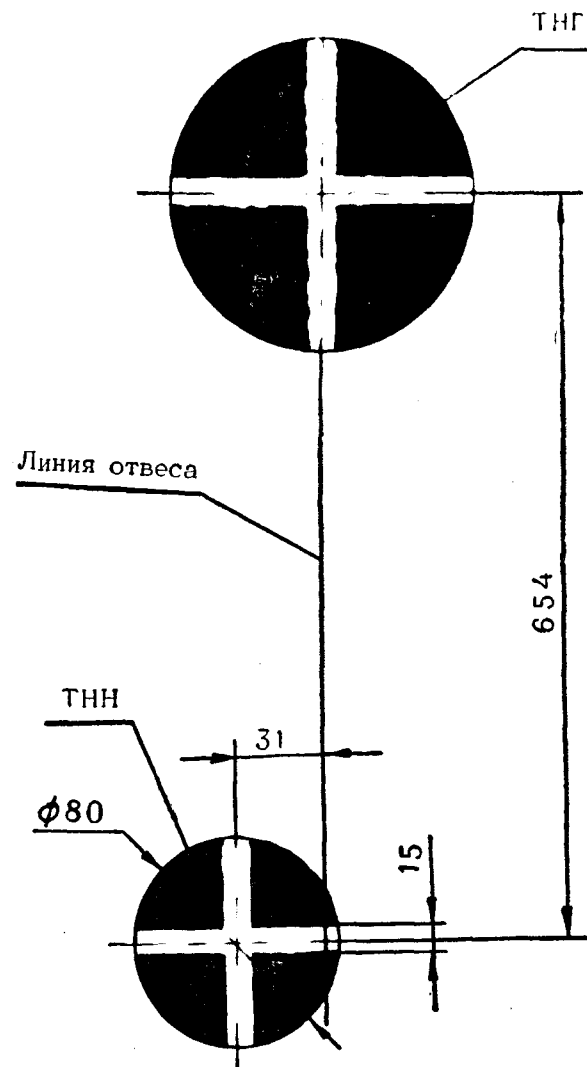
Схема выверочной мишени (щита для выверки прицела НСПУ):
